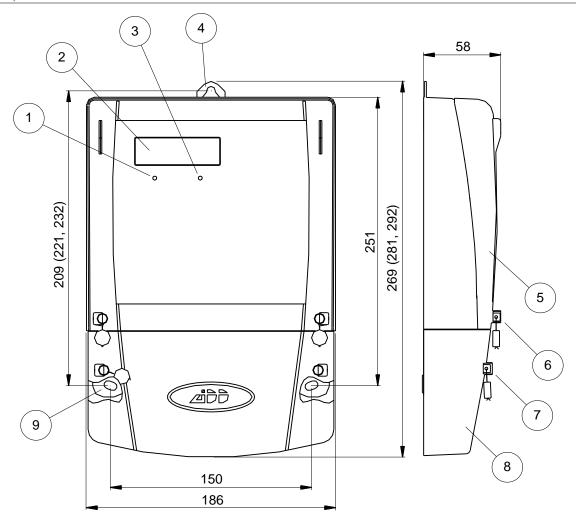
Внешний вид, габаритные размеры и места установки пломб на корпусе типа 3
